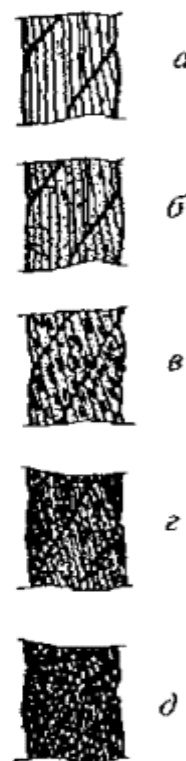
Поверхностная коррозия проволок каната крестовой свивки:
